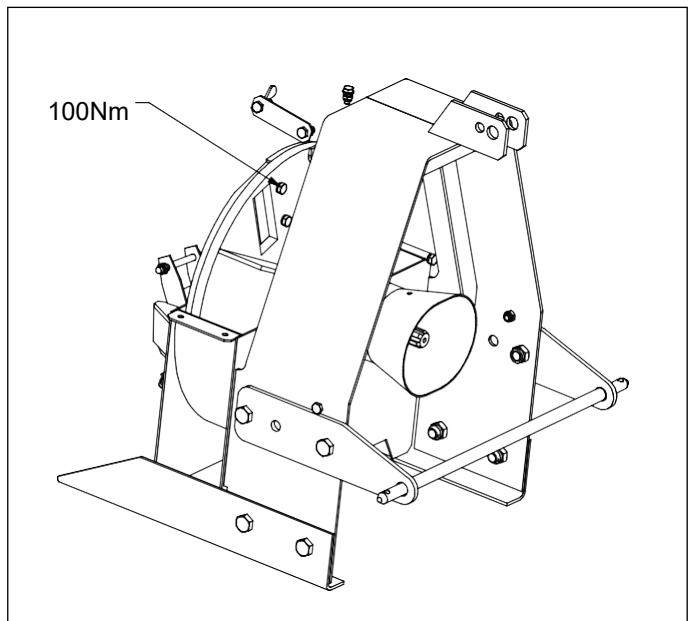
Entfernen der Messerbefestigungsschrauben (M12)
